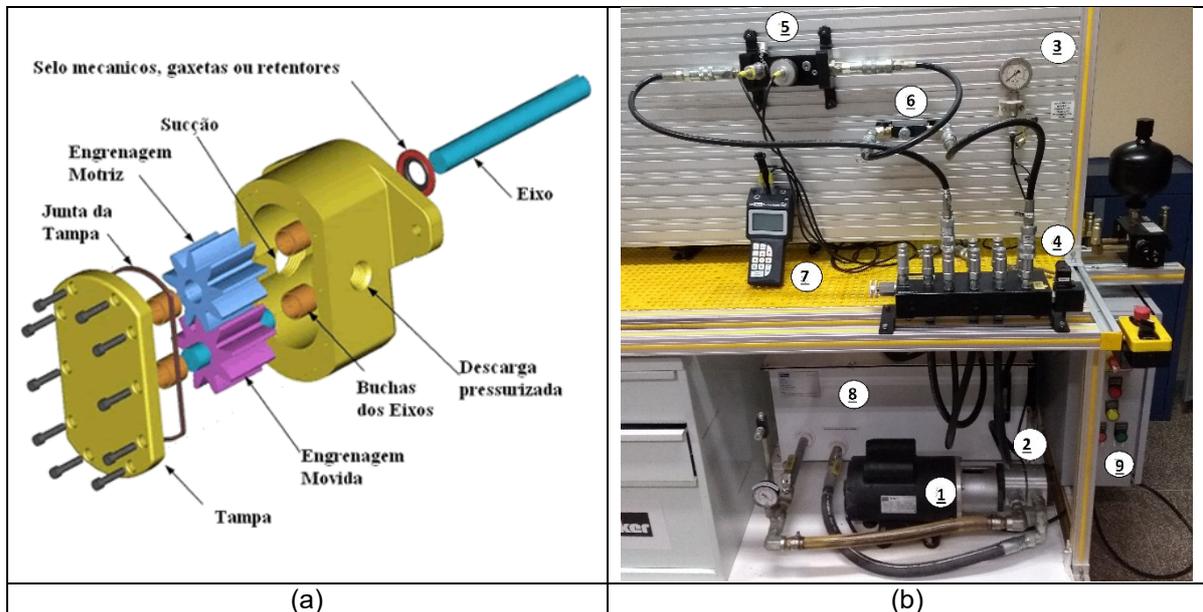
(a) – Bomba de engrenagem (b) – Experimento montado na bancada
